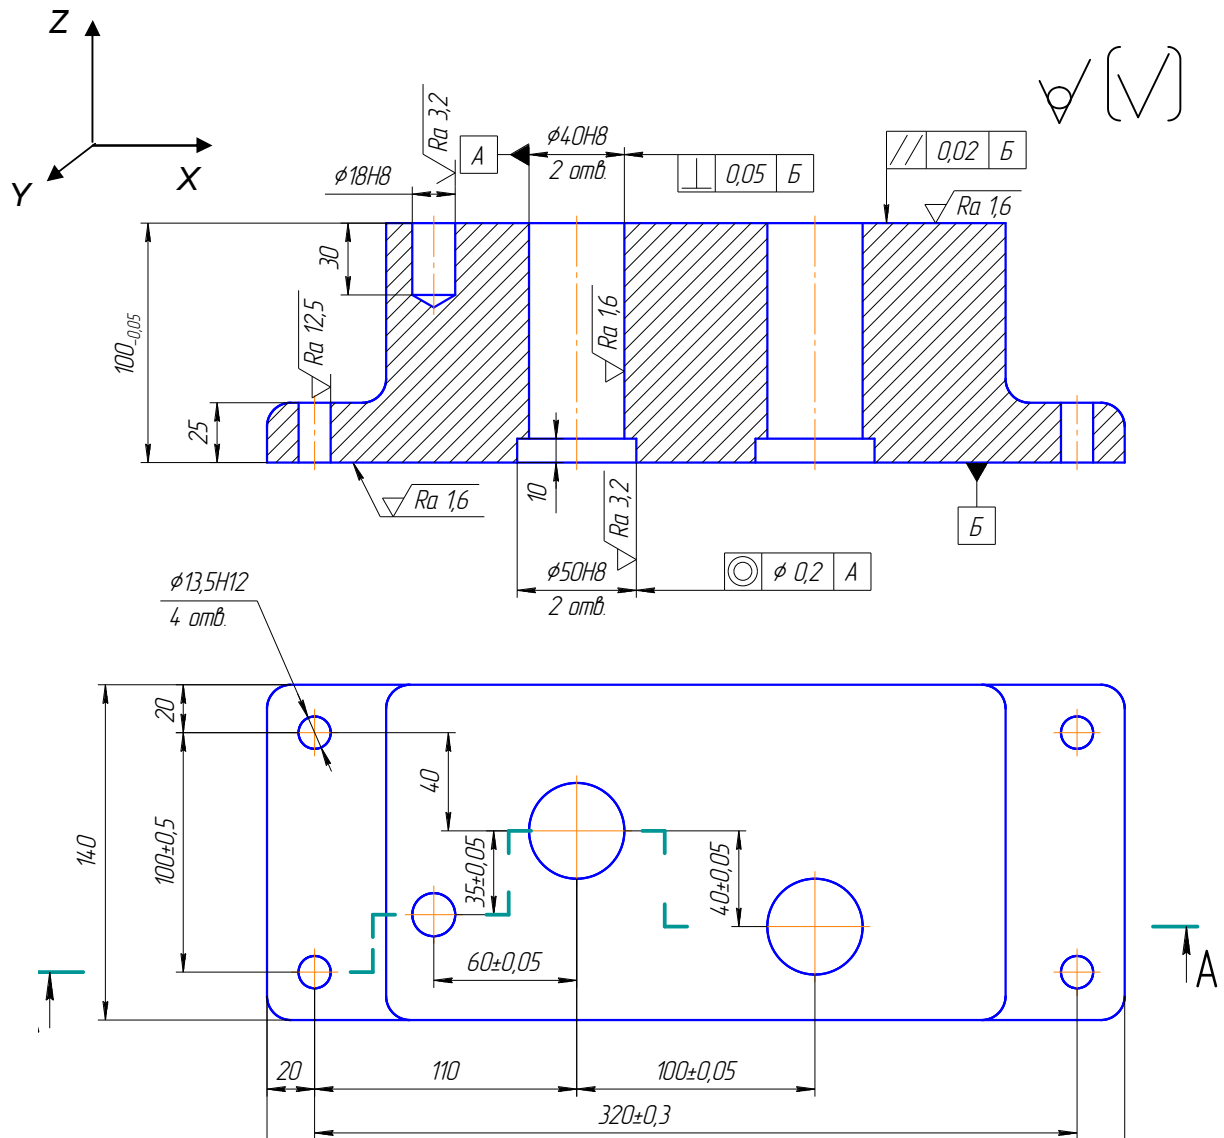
Розтушування розмірів на кресленні деталі, яка має оброблені та необроблені поверхні (вихідна заготовка — вилівок)
